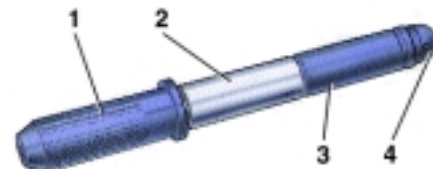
Установка поршневого пальца двигателя мод. 2106-70 на приспособление, для запрессовки его в поршень и головку шатуна: 1 – валик приспособления; 2 – поршневой палец; 3 – направляющая; 4 – упорный винт
